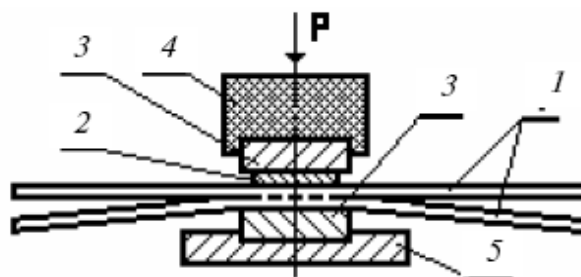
Схема зварювання плівок: *1* - зварювані плівки; *2* - нагрівач; *3* - еластичні прокладки; *4* - рухомий електрод; *5* - нерухома опора
